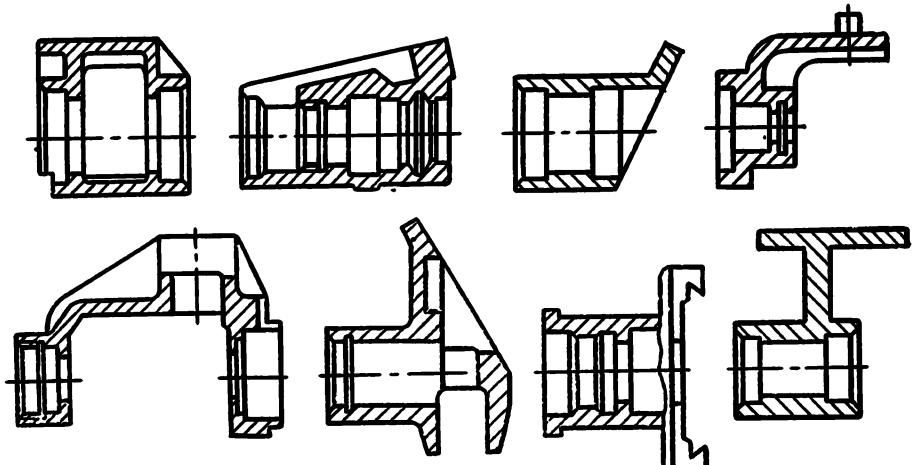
Группа деталей со сходными обрабатываемыми поверхностями
